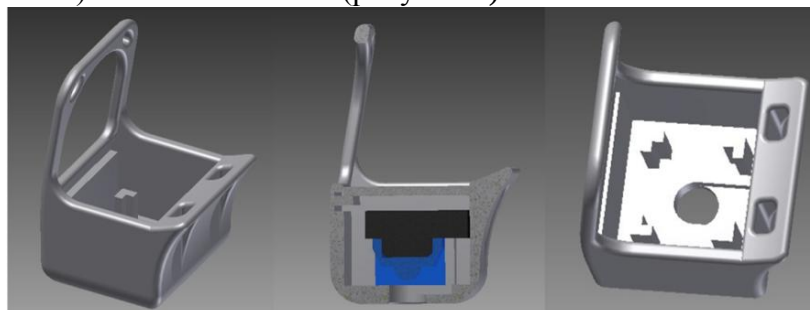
Сборка корпуса в САПР Autodesk Inventor
